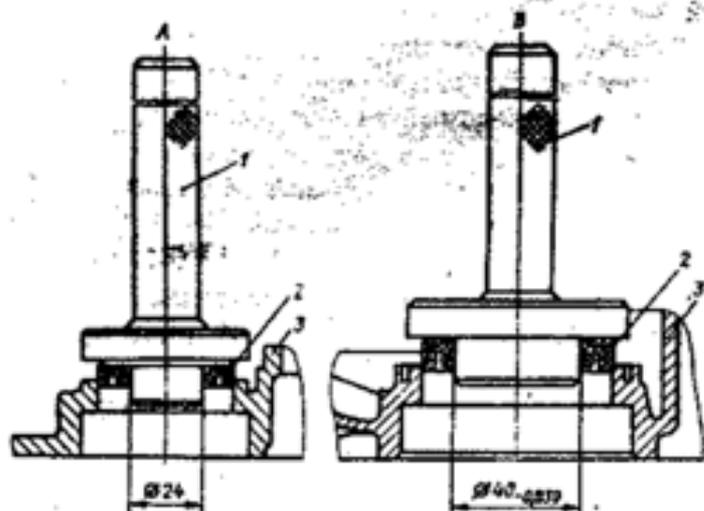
Запрессовка манжеты: А - ведущего вала: 1 - оправка М9840-784; 2 - манжета; 3 - картер сцепления; В - полуоси: 1 - оправка М9840-783; 2 - манжета; 3 - картер коробки передач
